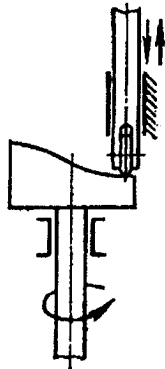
Кулачковий механізм барабанного типу з робочою поверхнею на торці кулачка
